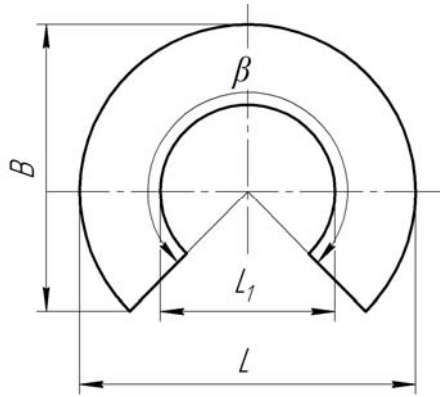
Схема розгортки конічного невідбортованого днища
